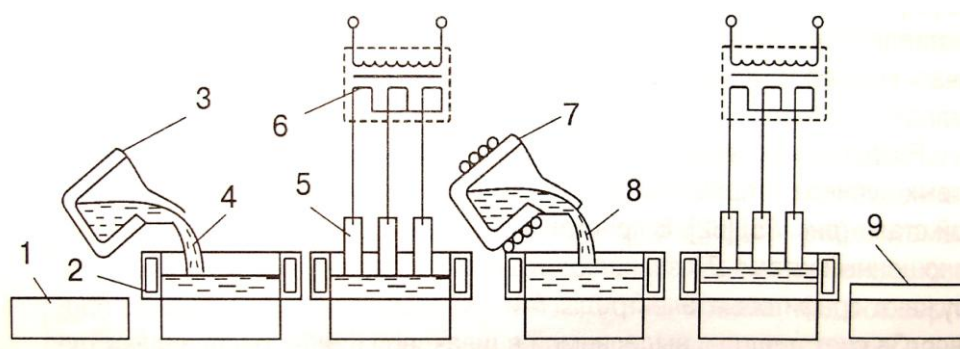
Схема получения многослойных заготовок ЭШН заливкой жидкого металла на твердую подложку:
